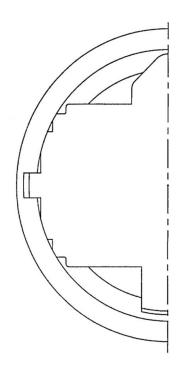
Пример изготовления тонкостенной детали – основание (заготовка)
